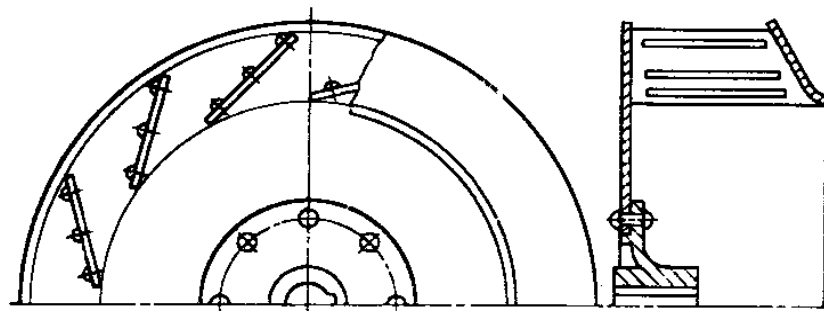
а. Рабочее колесо с прямыми листовыми лопатками, отклоненными назад
